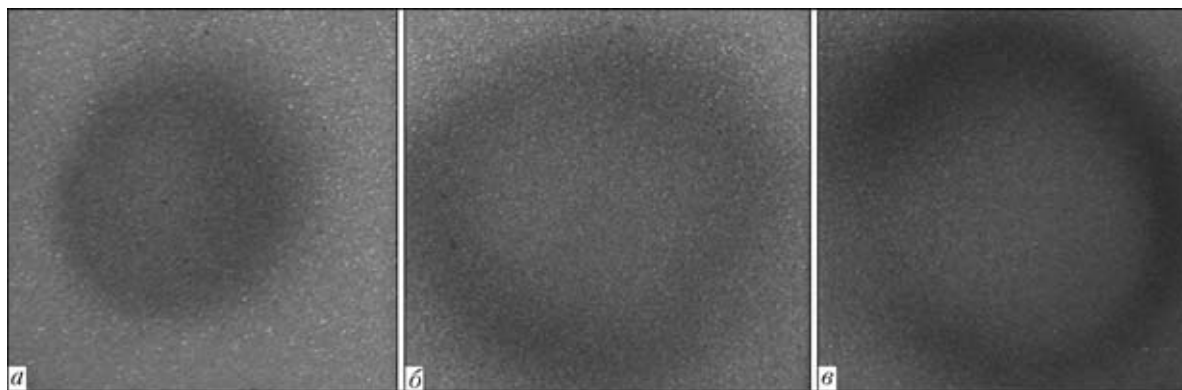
Пятно напыления при нанесении покрытия с использованием насадки (а), цилиндрической части насадки (б) и без нее (в)
